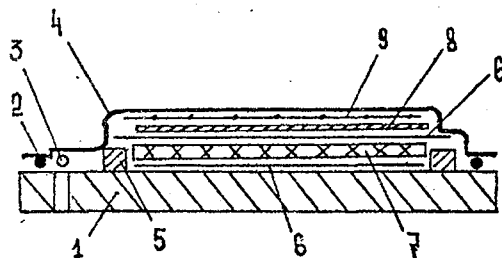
Схема технологического пакета: 1 — форма; 2 — уплотнитель; 3 — боковое выпускное отверстие; 4 — диафрагма; 5 — ограничительная рамка; 6 — пленка; 7 — пакет заготовок; 8 — цулага; 9 — дренажный слой
